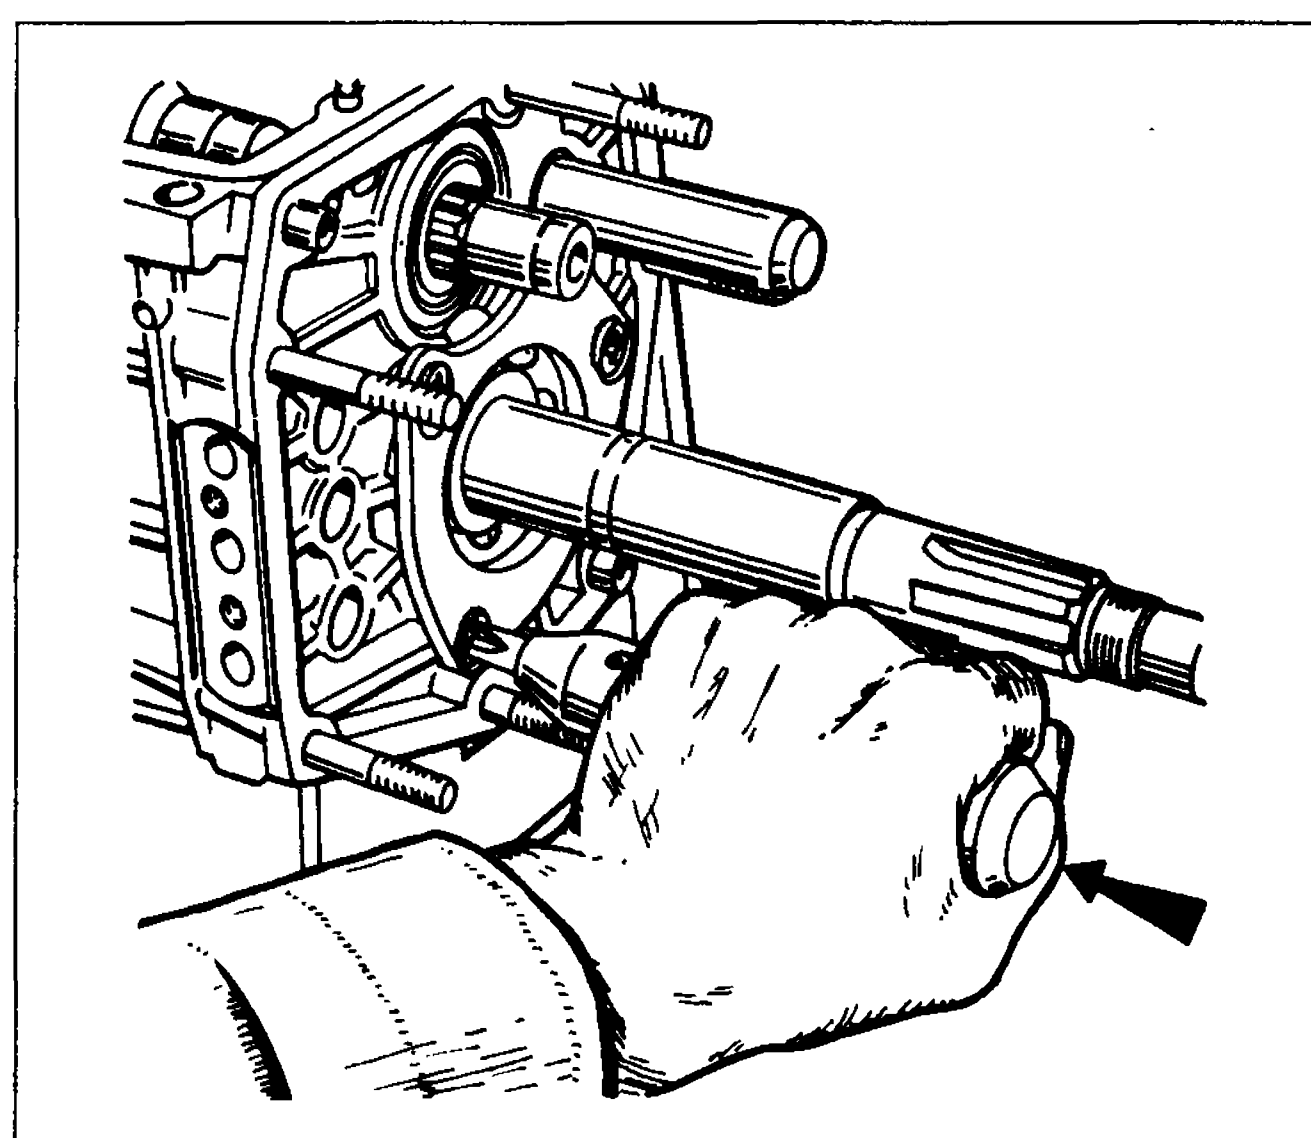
Снятие стопорного пружинного кольца шестерни заднего хода с промежуточного вала
